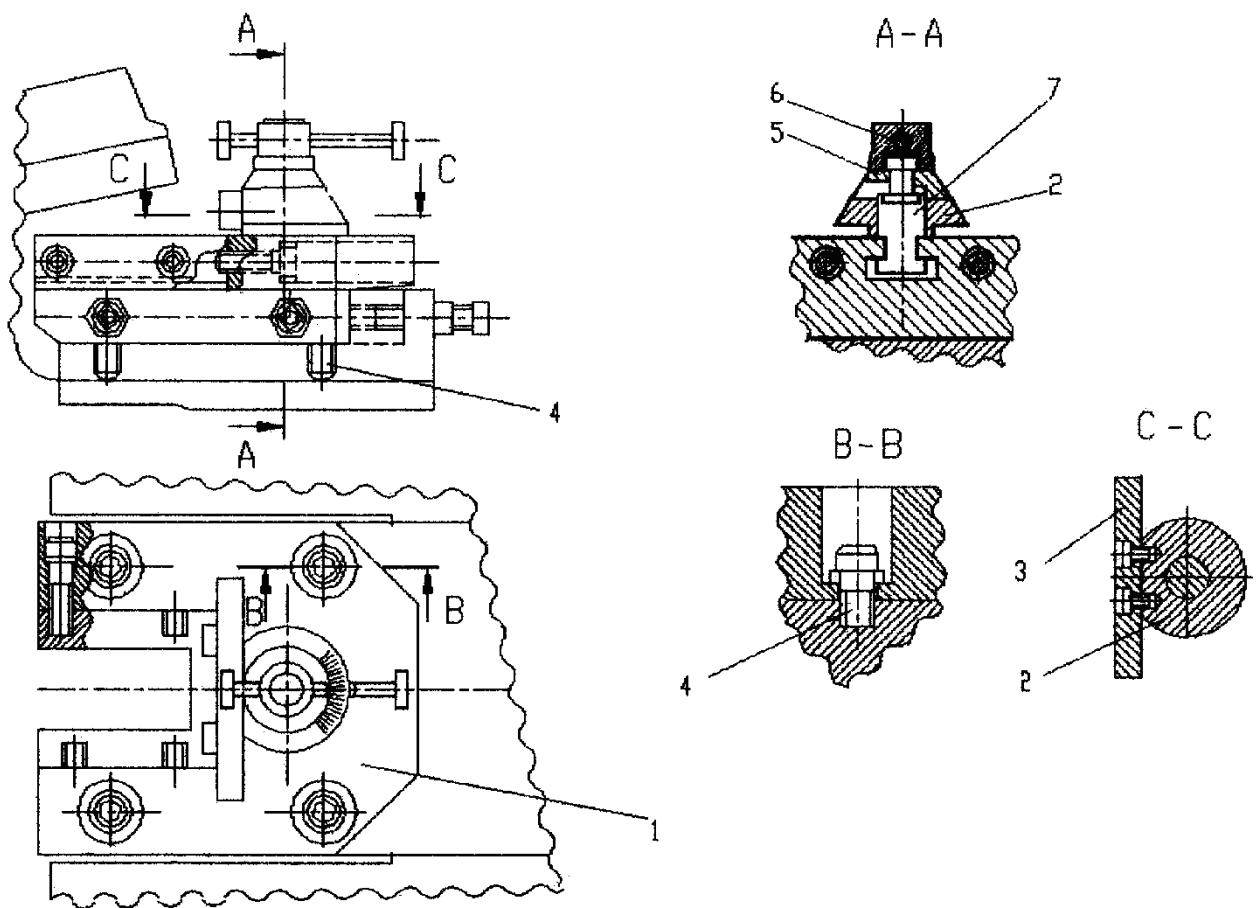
Приспособление для пробивки пазов прямоугольной формы.
